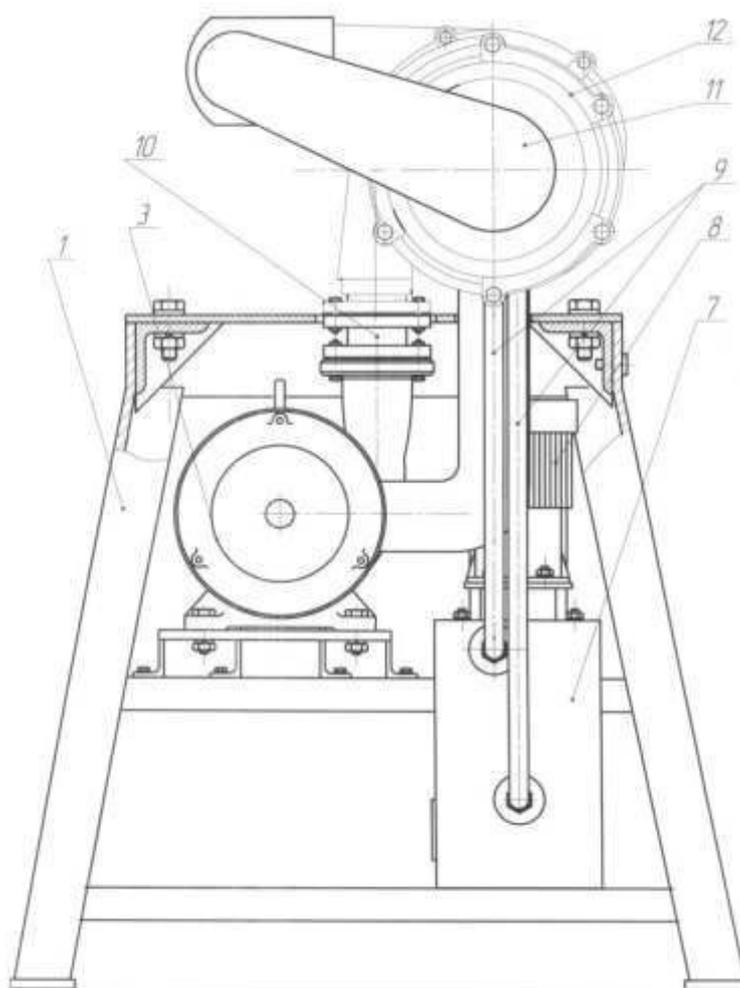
Стенд для обкатки ТКР (вид)
